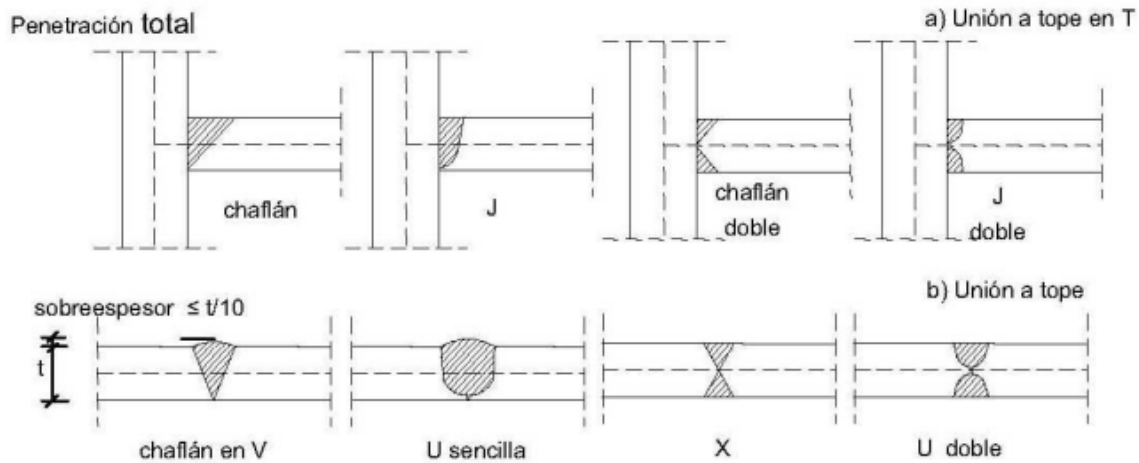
Tipos soldaduras de penetración total [7]
